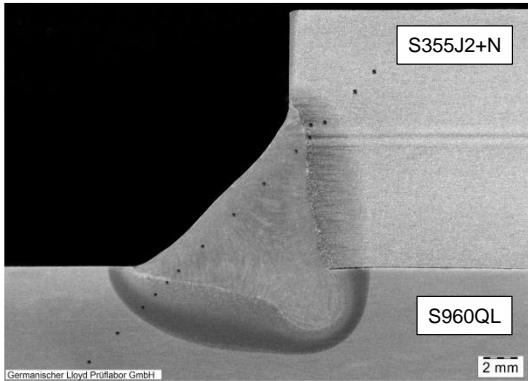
Makroschliff einer Flankenkehlnaht
